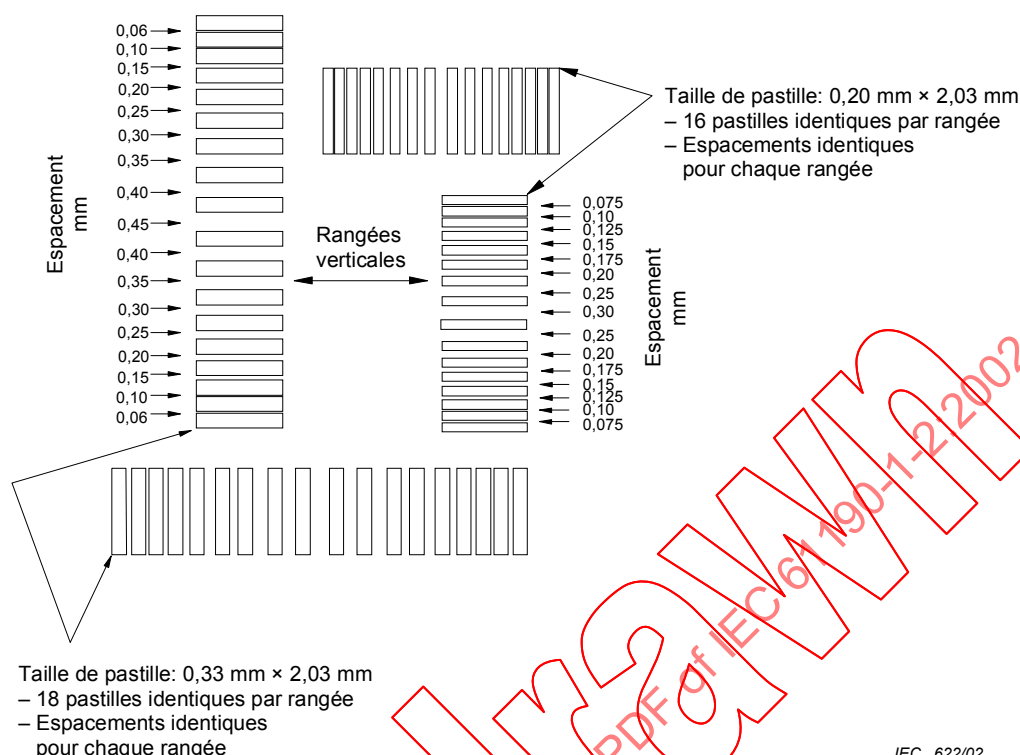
Epaisseur du pochoir de l'essai de glissement – 0,10 mm
